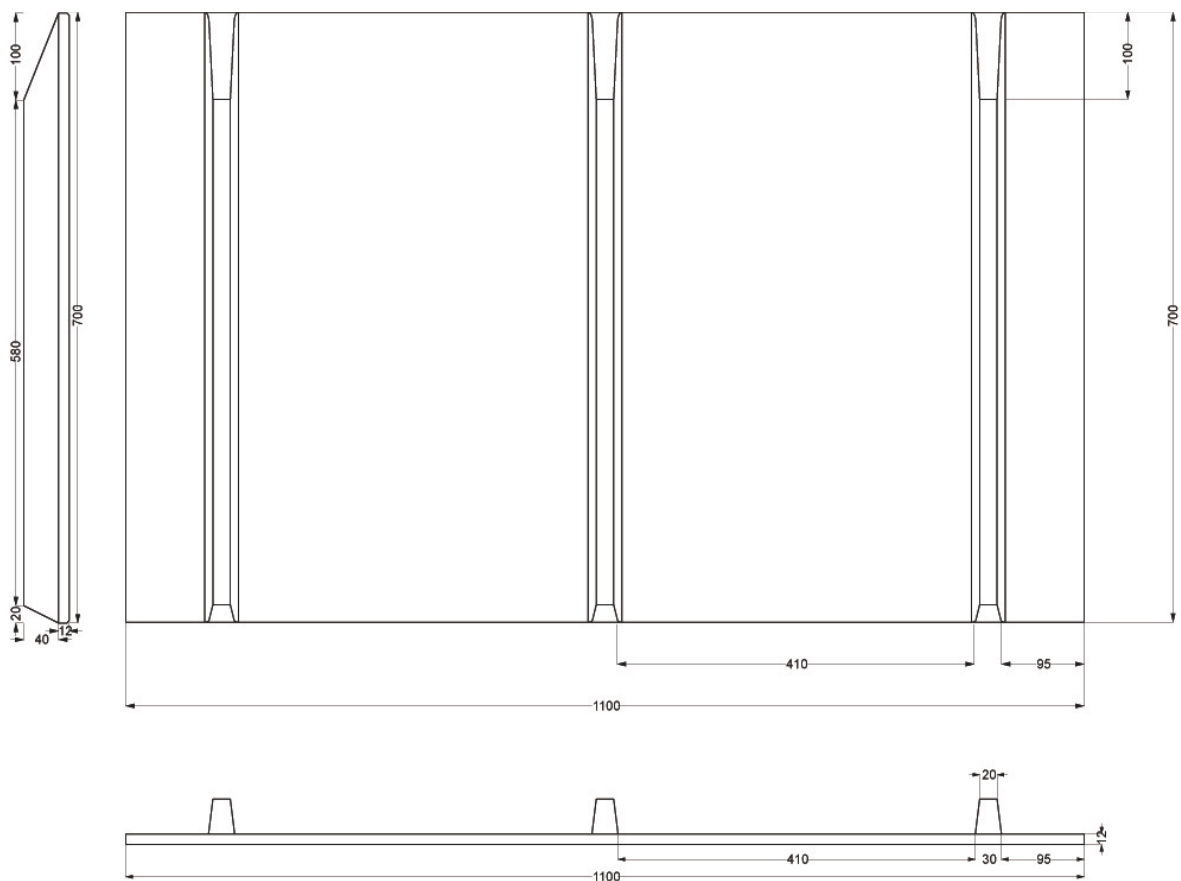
Ukotvení k radiátoru - zkosená deska
